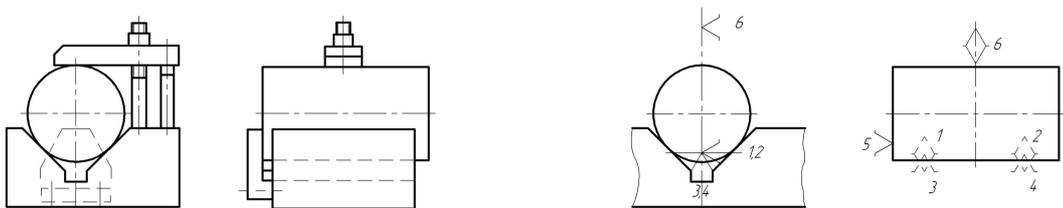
Установка вала в призме: 1 – 6 – опорные точки
